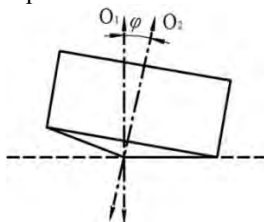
Схема движения главного штампового инструмента в DEFORM-3D
